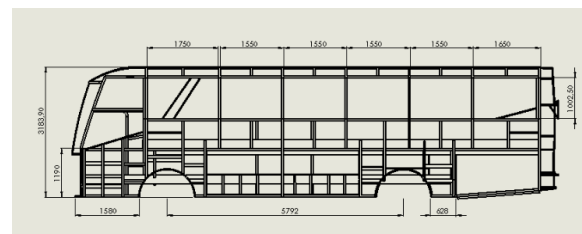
Dimensiones de la carrocería desde la vista frontal
